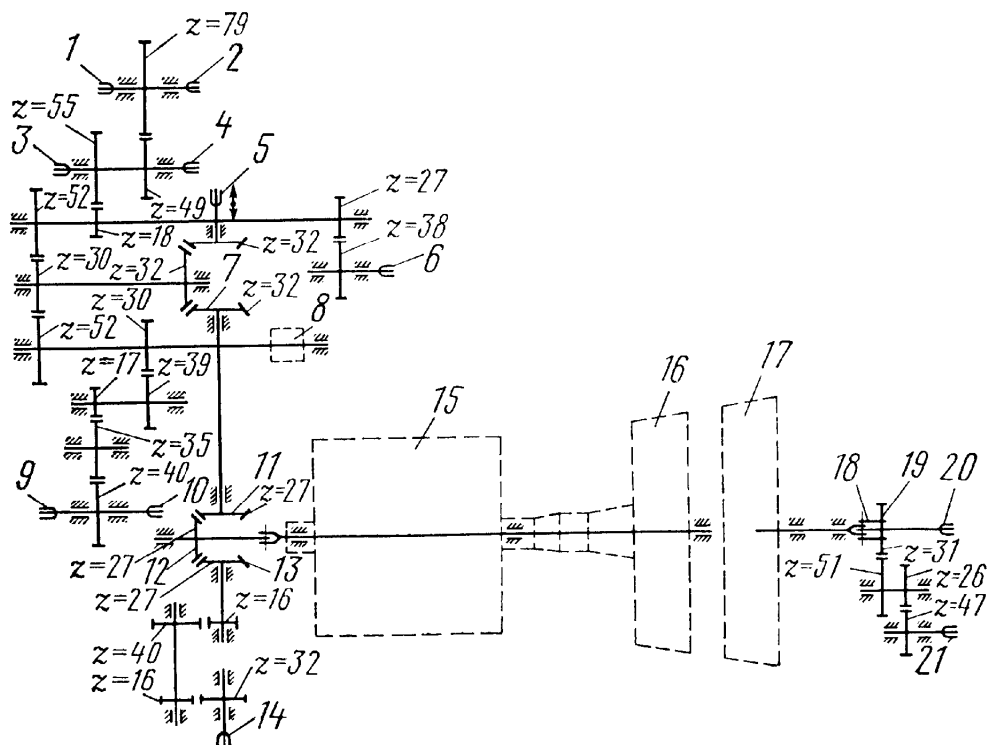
Кинематическая схема двигателя и приводов агрегатов:
